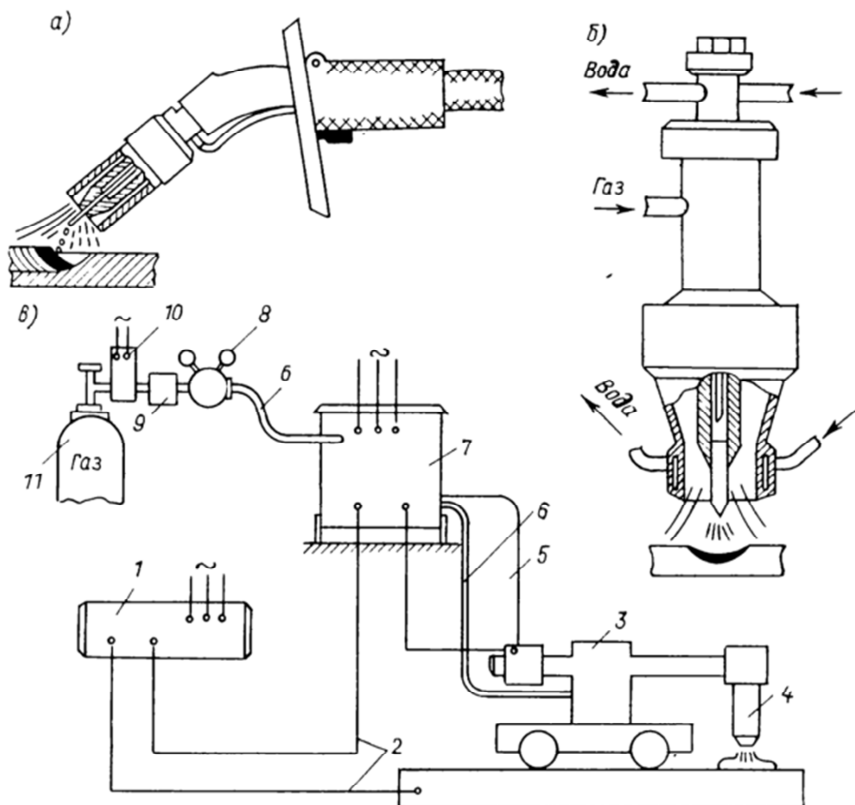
Схема установки для сварки в защитных газах;
